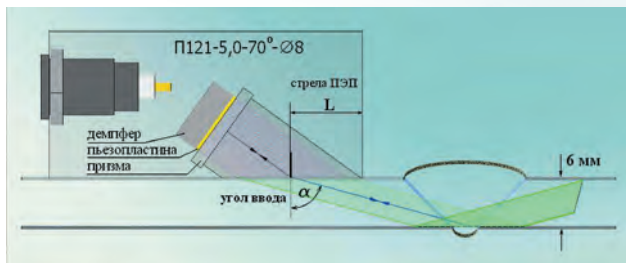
Прозвучивание корня сварного соединения наклонным совмещенным преобразователем
